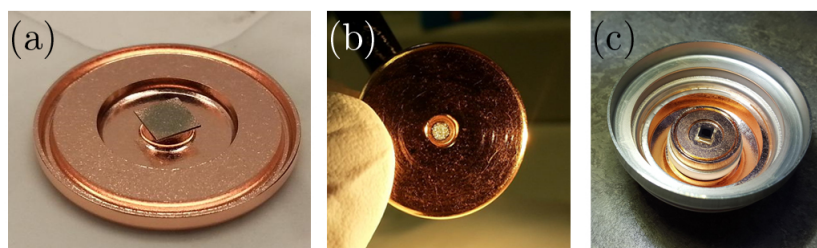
Figure a et b* : smart-windows brasées par TED sur un disque en cuivre qui permet de finaliser le montage d'une fenêtre innovante en diamant sur un tube à rayons X. *Figure c* : soudage laser du disque en cuivre sur la tête du tube.
